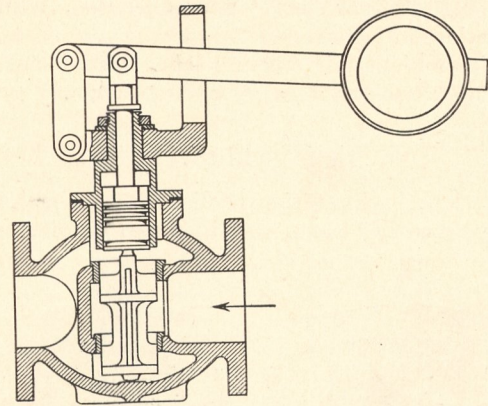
Dampfdruckreduzierventil mit Gewichtsbelastung. Ausführung: Schäffer & Budenberg, Magdeburg-Buckau.
